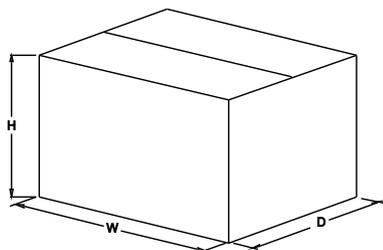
Габаритные размеры упаковочной тары
